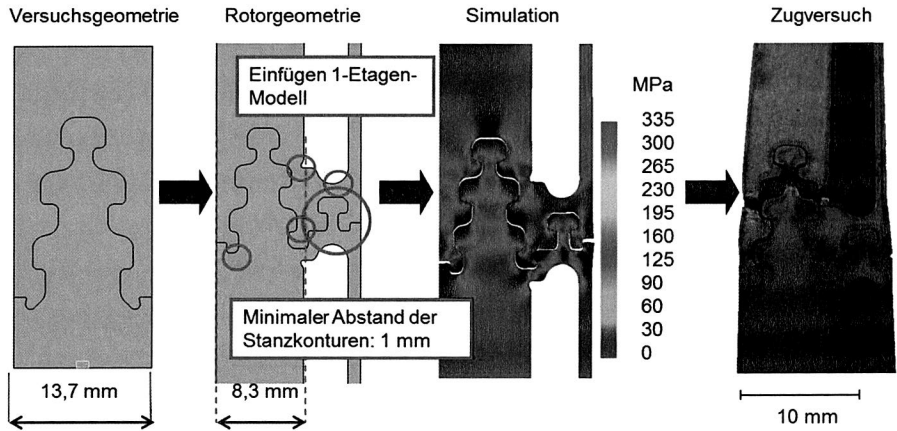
Anpassung in die Rotorgeometrie – Optimierung und Zugversuche. [89]
